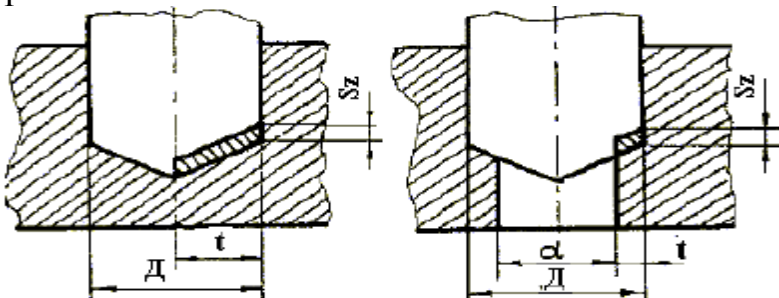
Схема резания при сверлении и рассверливании
